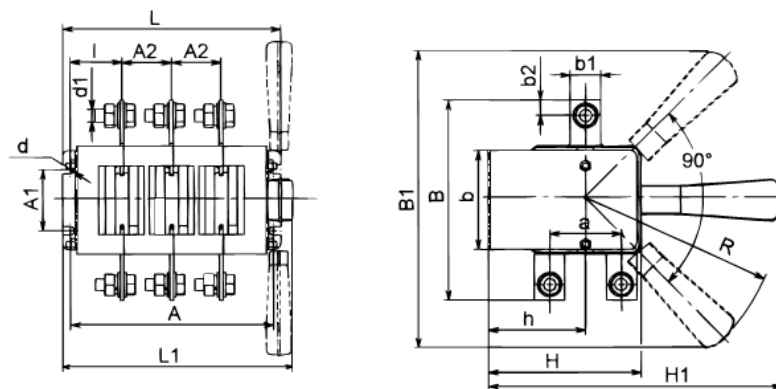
Б Выключатель-разъединитель на два направления трехполюсный с боковой рукояткой
